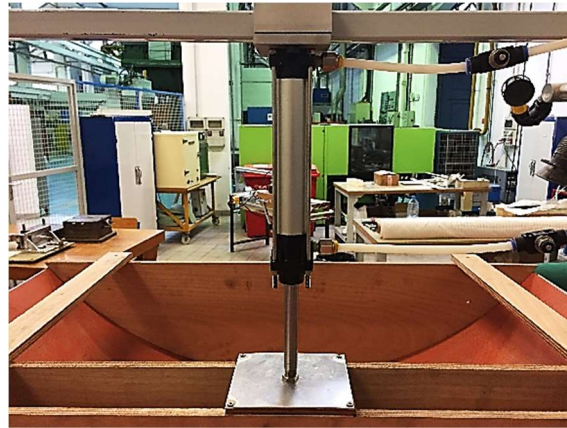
Vérin pneumatique qui assure le mouvement du contre-moule.
